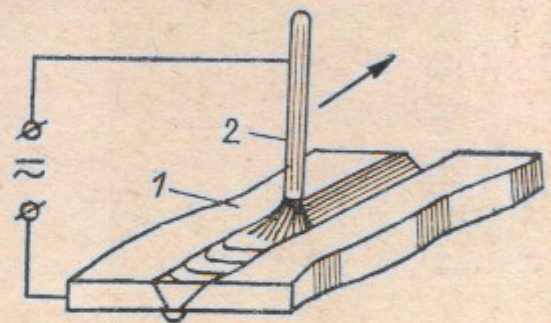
Сварка металлическим электродом с покрытием.
